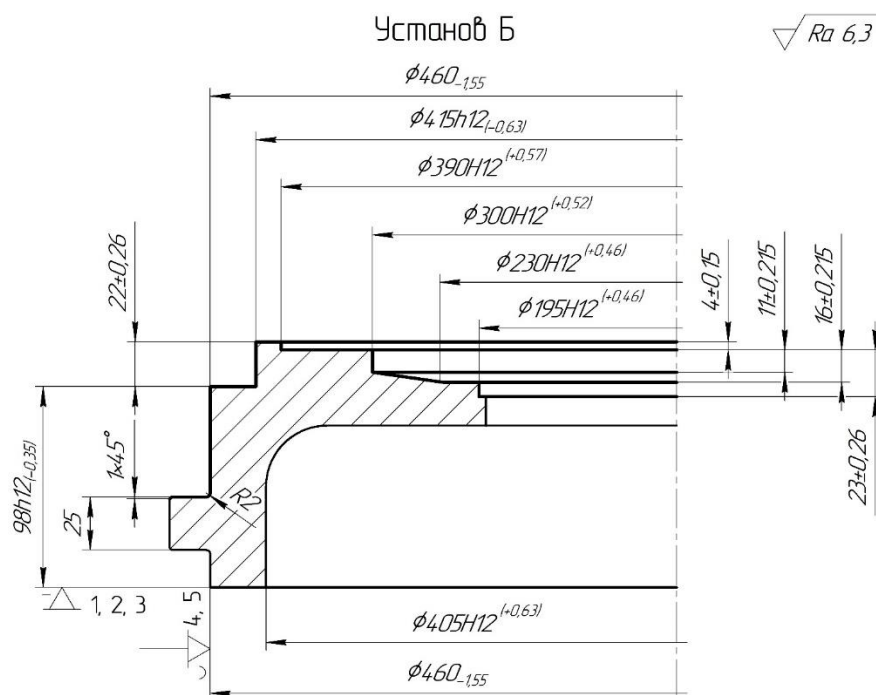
Ескіз заготовки на операції 015. Установ Б
